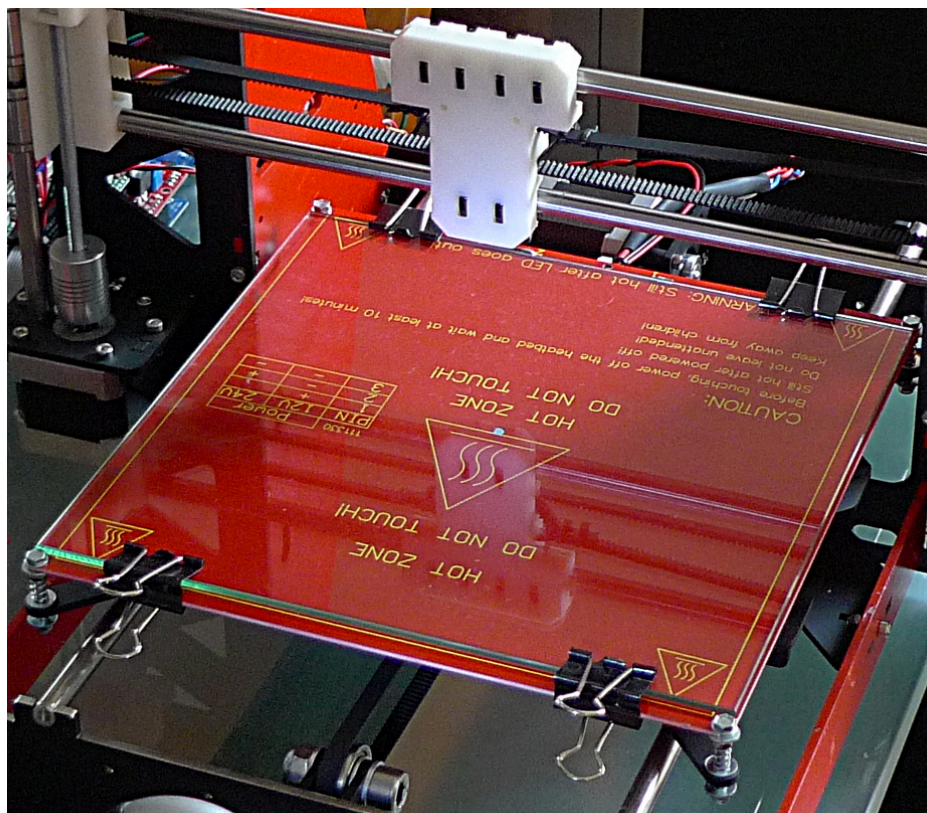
Mesa aquecida PCB montada com superfície de vidro
